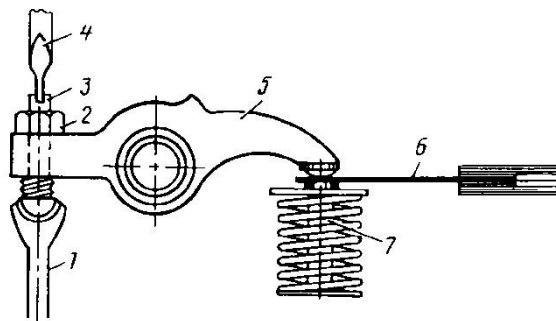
Регулировка зазоров в газораспределительном механизме: 1-штанга; 2 - контргайка; 3 - регулировочный винт; 4 - отвертка; 5 - коромысло; 6 - шуп; 7 – клапан
